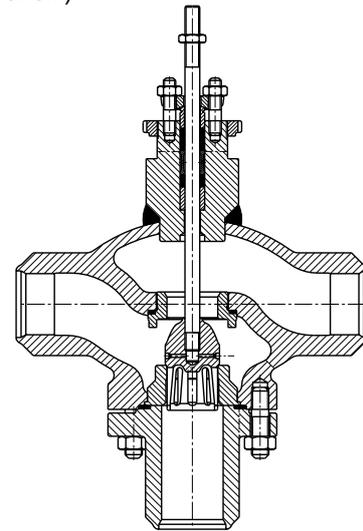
Регулирующий клапан с выводами для сварки
